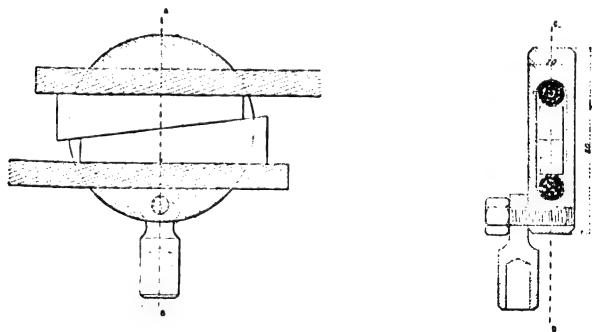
et 15. — Coupe suivant CD et coupe suivant AB d'une pièce de raccord pour câbles de 25 à 70 mm<sup>2</sup> de section.
